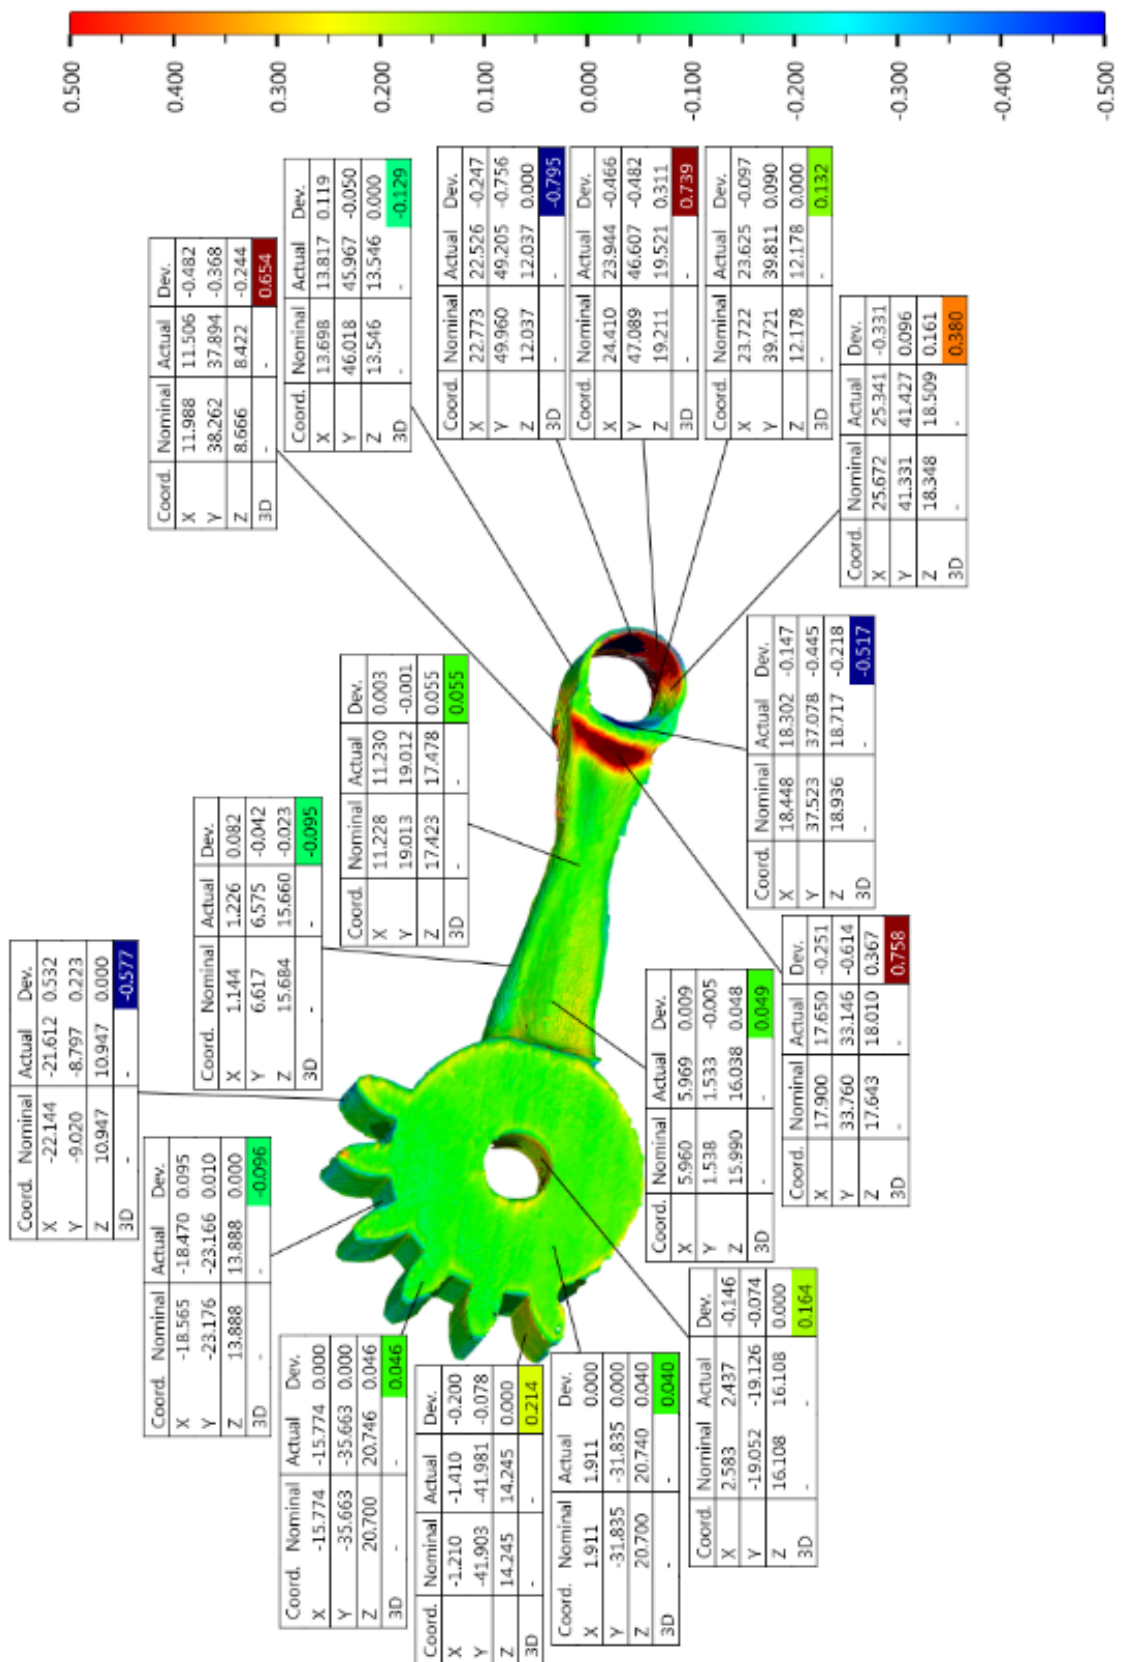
Controlo dimensional e geométrico da haste com engrenagem
